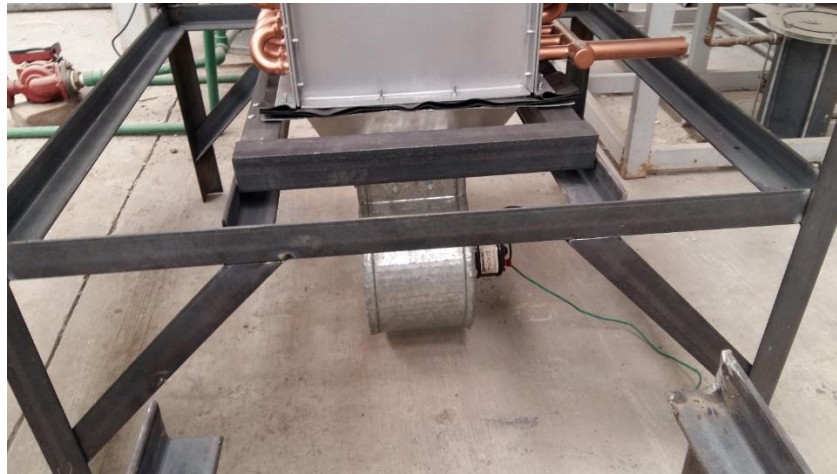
Carriles colocados en el marco inferior, con parte frontal sobrante
